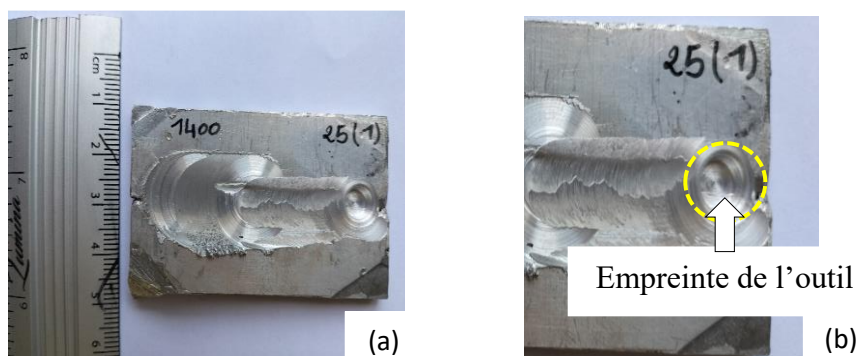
(a) Eprouvette soudé / (b) Empreinte de l'outil.
